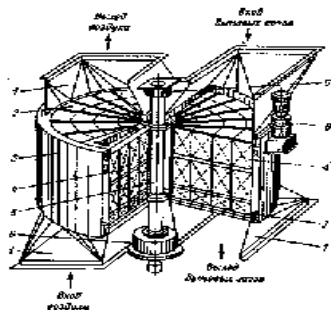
Вращающийся регенеративный воздухоподогреватель. 1 – корпус; 2 – барабан; 3 – корпус; 4 – набивка; 5 – вал; 6 – подшипник; 7 – уплотнение; 8 – электродвигатель.
